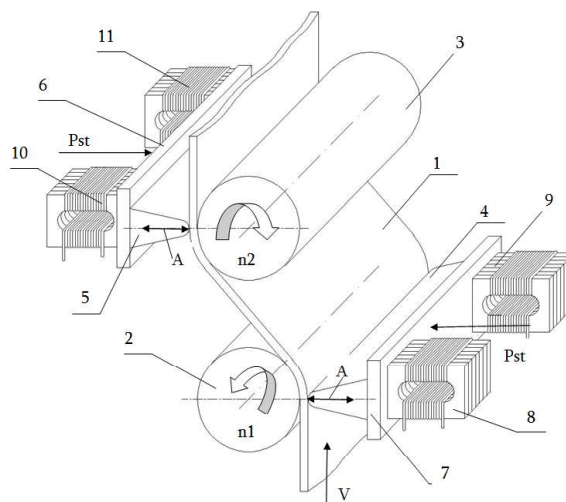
Схема осуществления способа повышения физико-механических свойств титановой фольги с применением УЗК [20]: 1 - обрабатываемый материал (титановая фольга), 2,3 – дополнительные валки, 4,5 - концентраторы преобразователей УЗК, 6,7 - преобразователи УЗК, 8,9,10,11 – трансформаторы преобразователей УЗК
